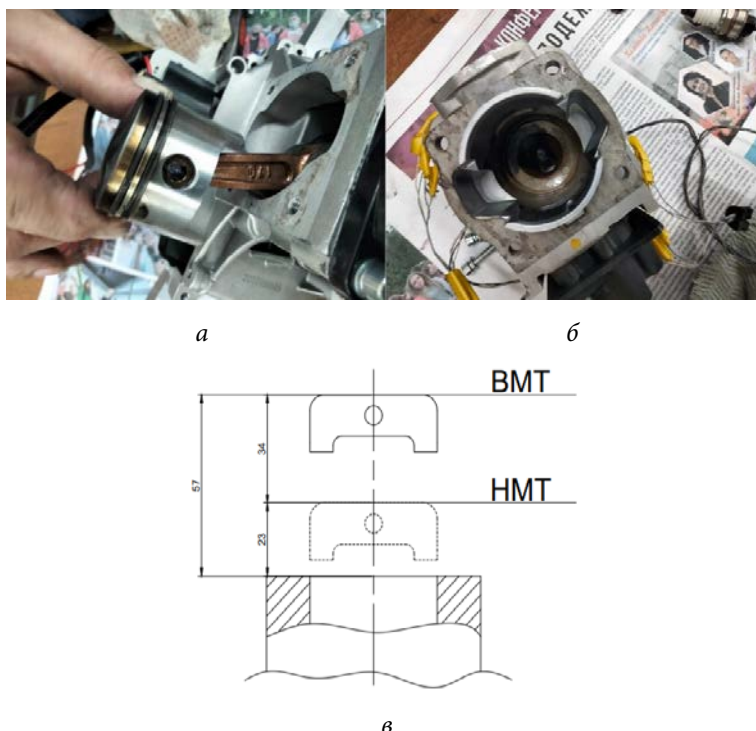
Измерение хода поршня (а) и диаметра цилиндра (б) двигателя Champion G052НТФ-II и схема измерения хода поршня (в):
